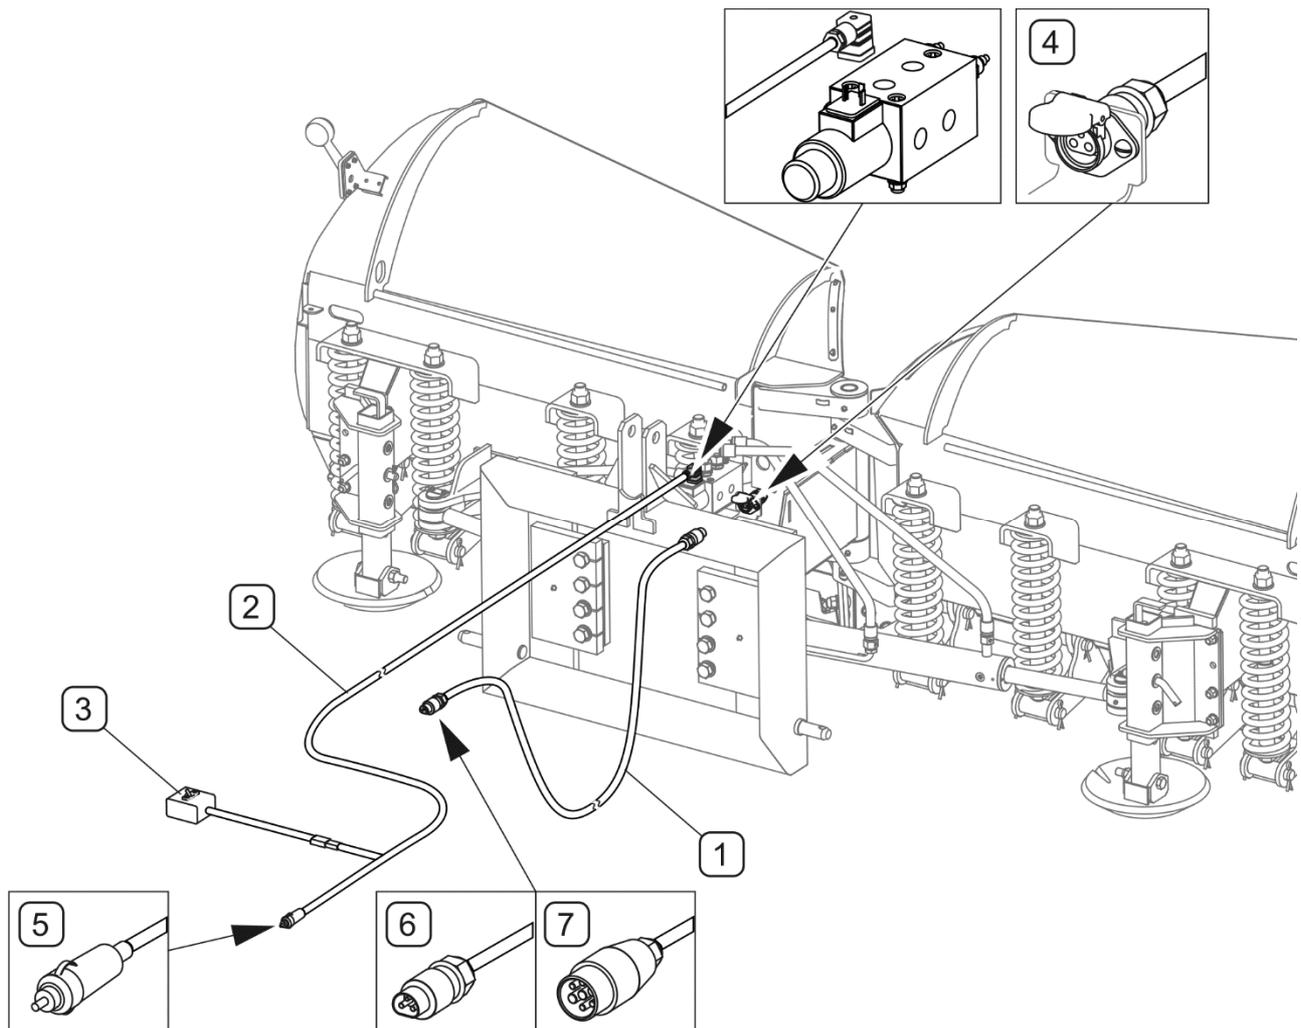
Raccordement de l'installation hydraulique
